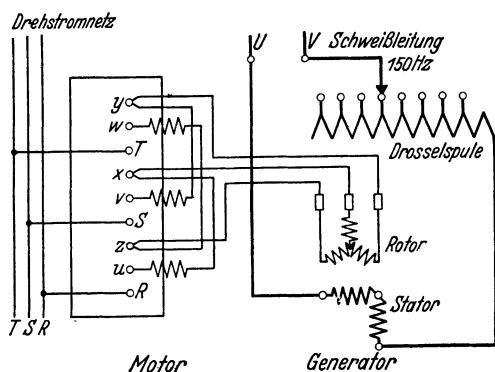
Schaltung einer Periodenumformer-Schweißmaschine.
